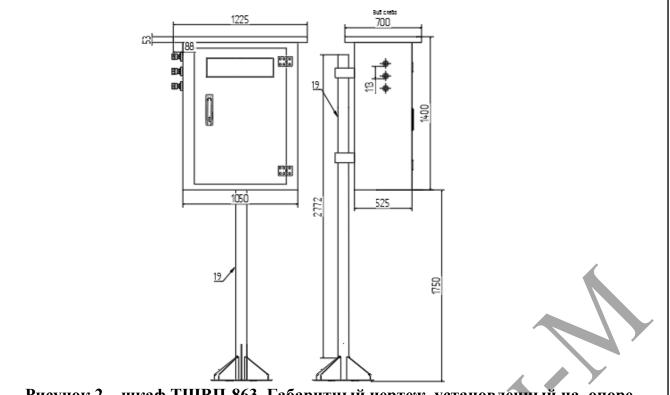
шкаф ТШВП-863. Габаритный чертеж, установленный на опоре..
